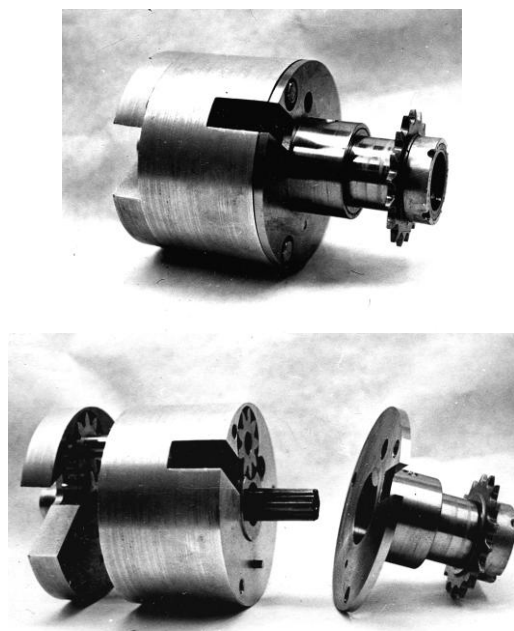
Модернизированный образец гидростатической коробки передач
